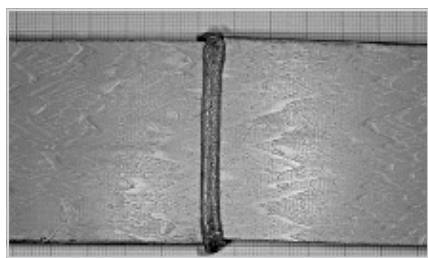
Сварной шов плоского листового образца из PEI, полученного при сварке нагретым инструментом встык
